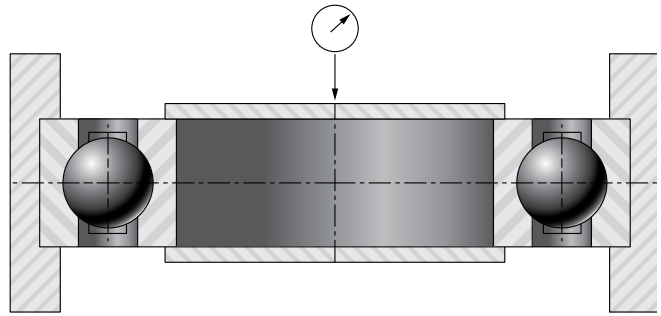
将轴承的一个轴承圈夹紧安装轴承，来确定轴向游隙
